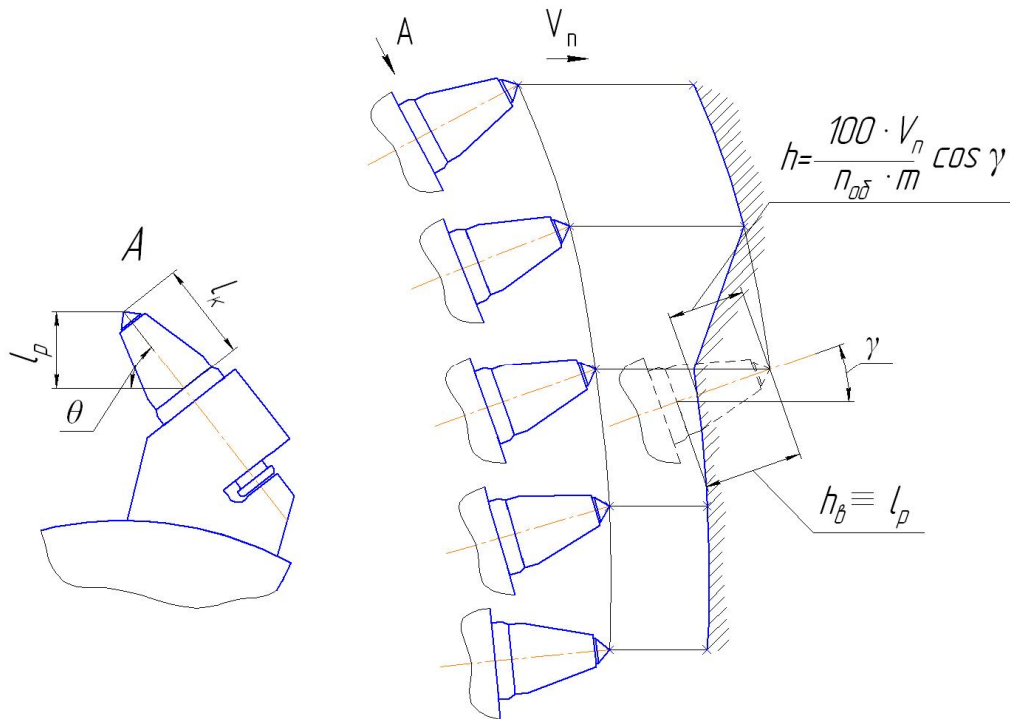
Формирование h на резцах фрезерного ИО аксиального типа
